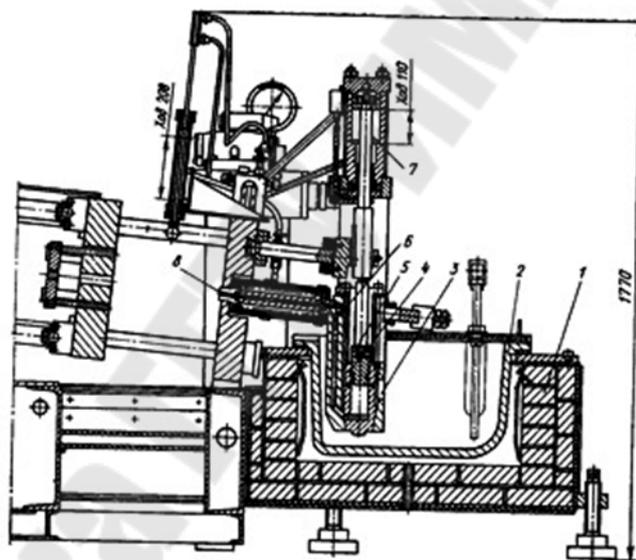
Механизм прессования машины с горячей камерой прессования
